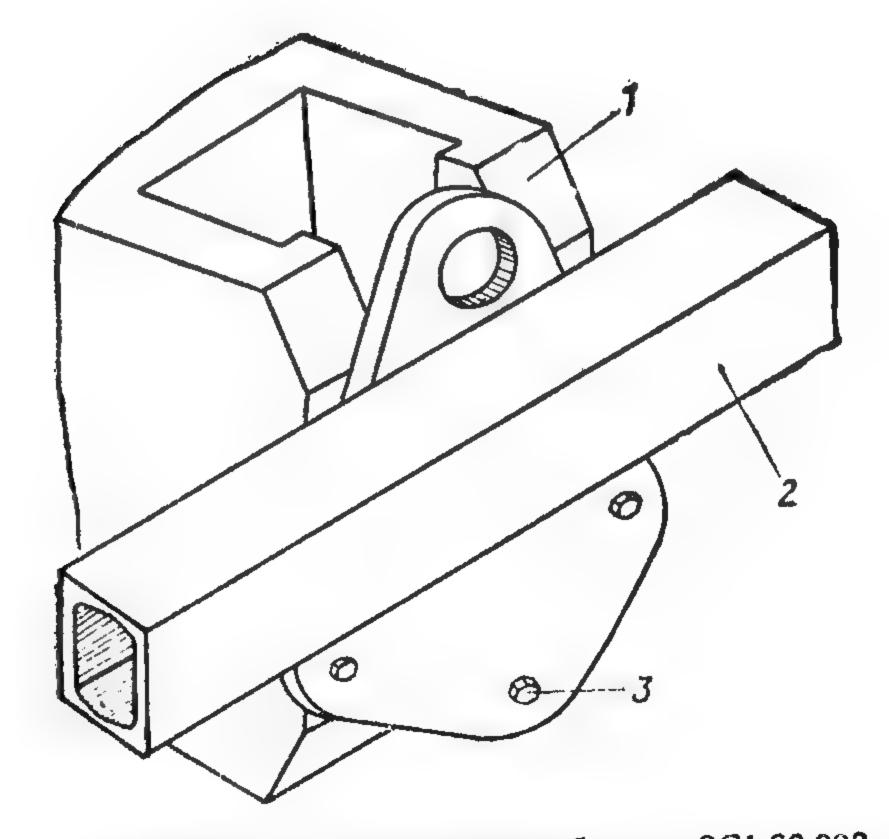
Установка приспособления 2С1.60.023; 1 -- казенник; 2 — приспособление 2С1.60.023; 3 — болт
